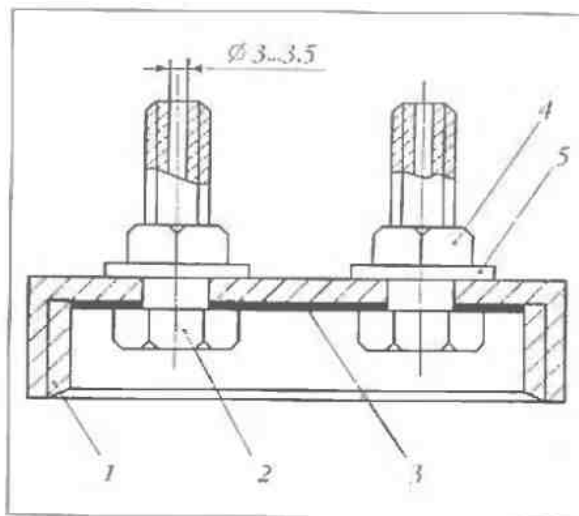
Схема крышки ресивера с входным и выходным патрубками, выполненными из болтов М8: 1 – крышка; 2 – болт; 3 – прокладка листовая резины; 4 – гайка; 5 – шайба
